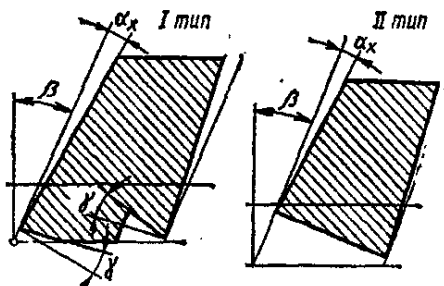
Форма заточки долбяков для косозубых колес
